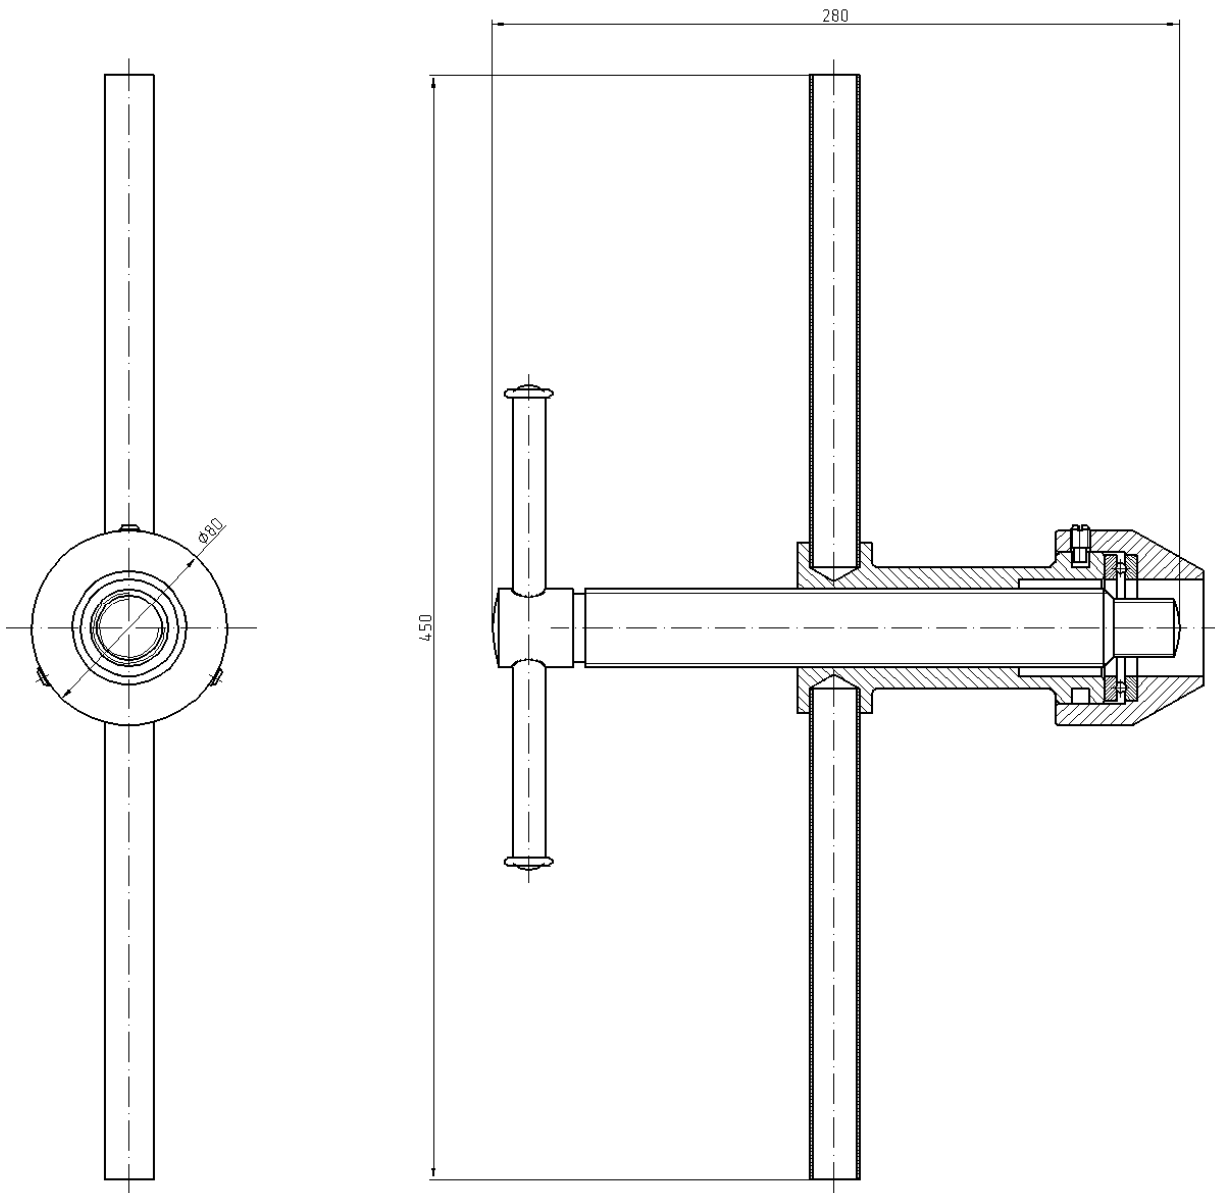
3M 7823-4291-01, Werkzeug zum Einpressen von Kettenrad und Nabe auf der Kurbelwelle
